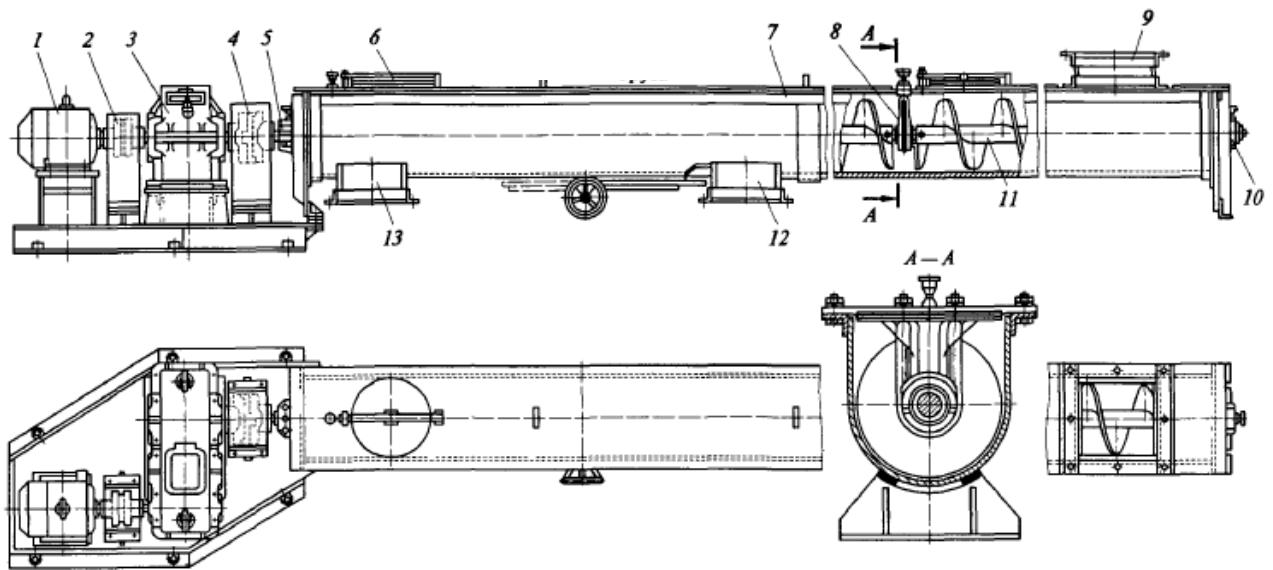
Конструктивна схема горизонтального ГК: 1 - електродвигун; 2, 4 - муфти; 3 - редуктор; 5, 8, 10 - опори; 6 - оглядовий люк; 7 - кожух; 9, 12, 13 - завантажувальний, проміжний та розвантажувальний патрубків, 11 - гвинт
